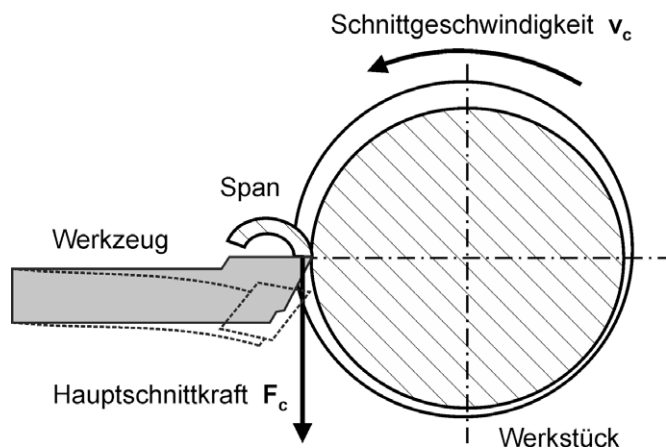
Verbiegung des Drehwerkzeugs unter der Hauptschnittkraft
